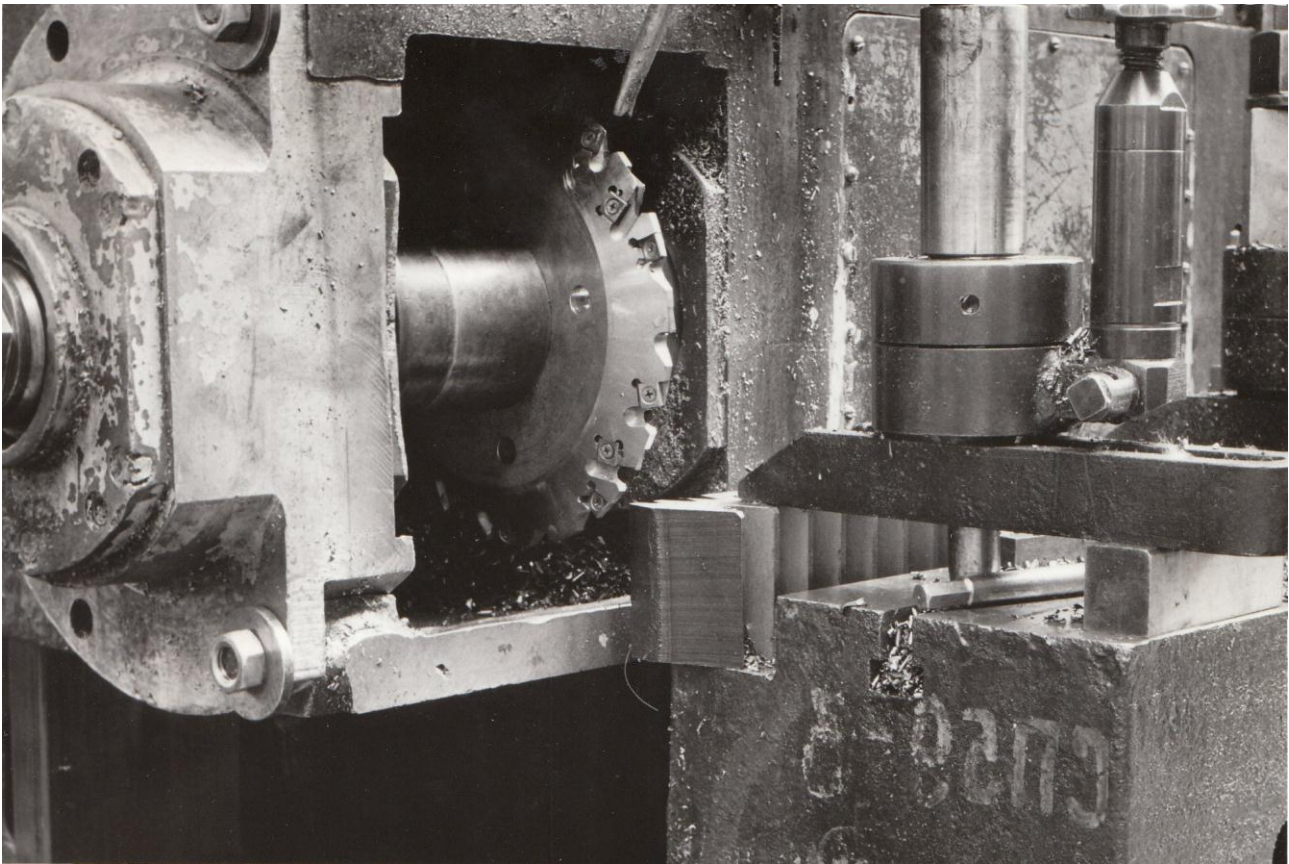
Профильная обработка зубчатых реек дисковой фрезой на рейкофрезерном станке мод. КУ-304
